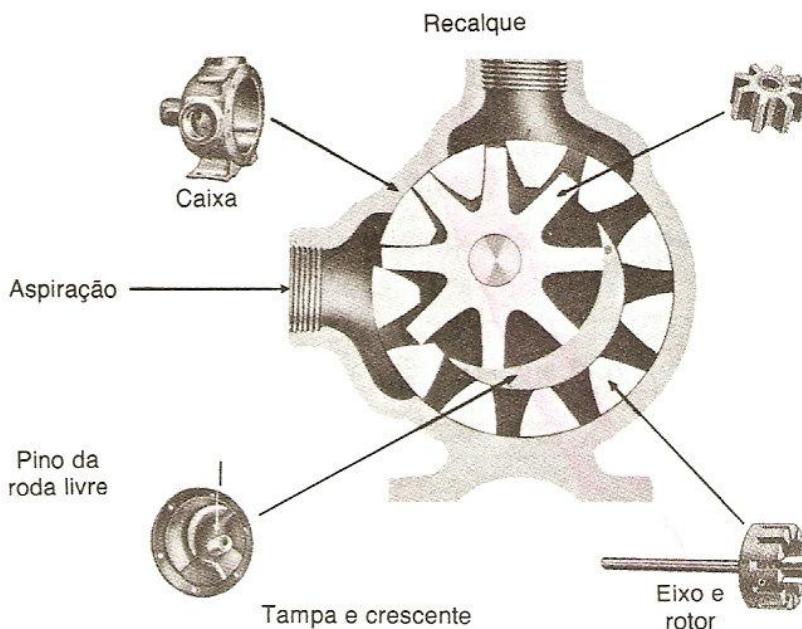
Partes de uma bomba de engrenagem interna.
